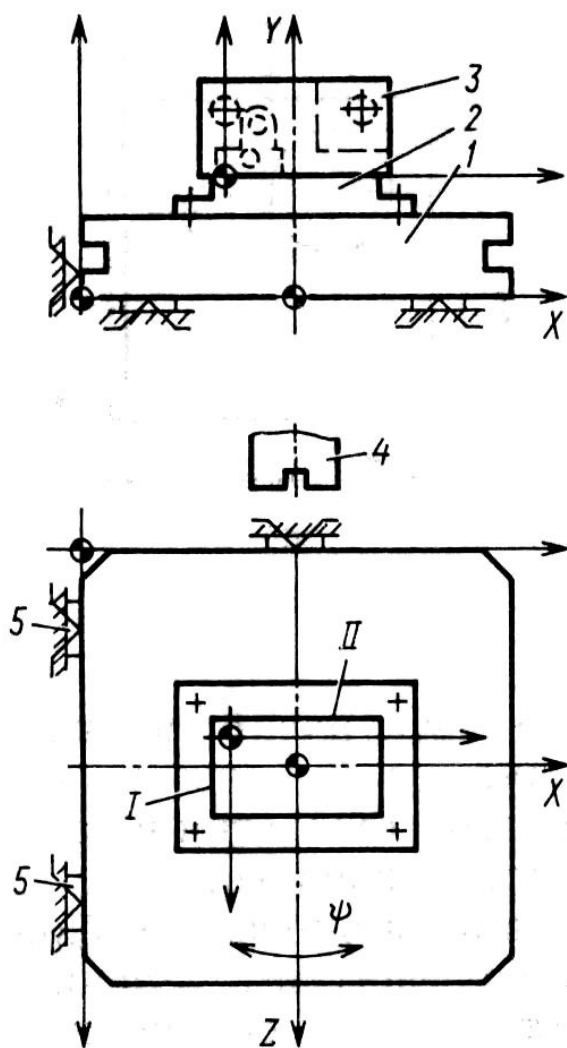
Установка заготовки на спутнике при обработке на многоцелевом станке 6904ВМФ2: 1 – спутник; 2 – подкладная плита; 3 – заготовка; 4 – шпиндель; 5 – опорные элементы приспособления; I, II – позиции для последовательной обработки заготовки со стороны I и II
